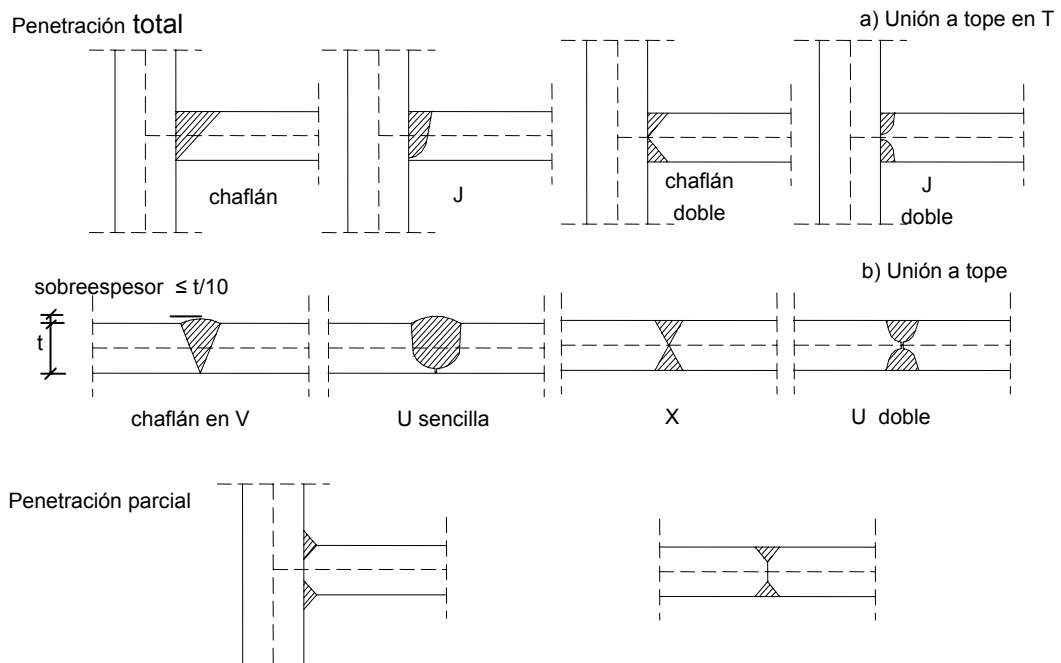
Soldadura a tope y formas de preparación
